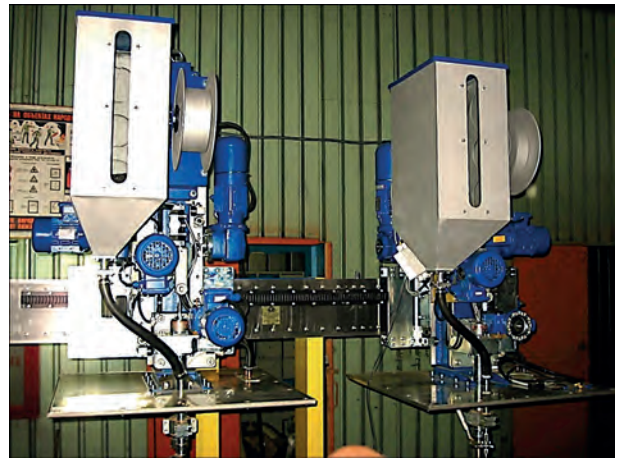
Загальний вигляд здвоєних зварювальних автоматів А1569М для автоматичного зварювання під флюсом у вузький зазор циліндричних виробів
